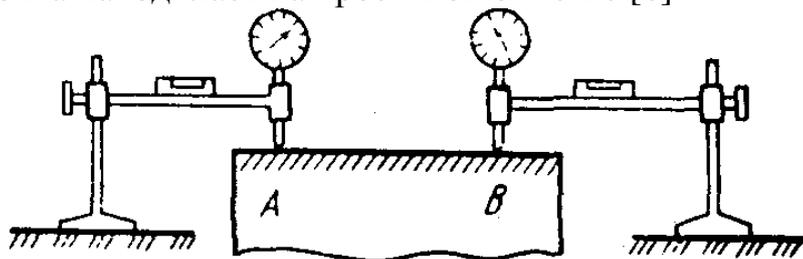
Схема индикаторного способа выверки конструкций и оборудования [6]
